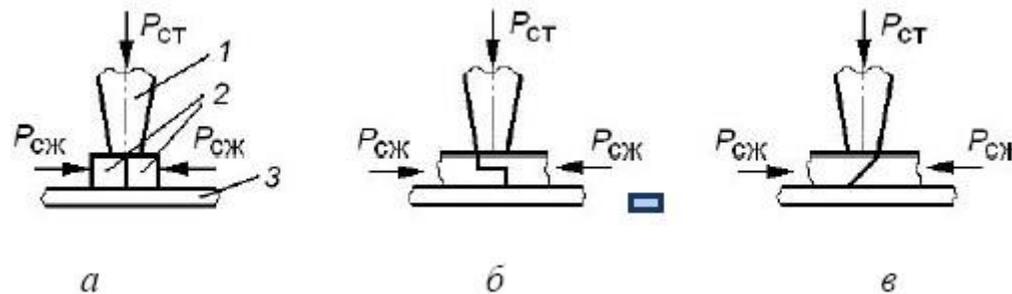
Конструкции стыковых соединений при сварке с дополнительным усилием сжатия $P_{сж}$, перпендикулярным $P_{ст}$: а – «плоский стык»; б – «замковое соединение»; в – соединение «в ус»; 1 – сварочный инструмент-волновод; 2 – свариваемые детали; 3 – опора
